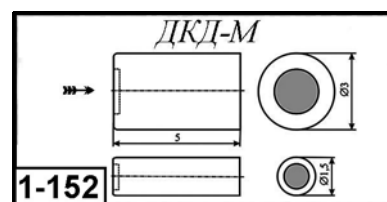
Внешний вид и габаритные размеры детектора ДКД-М
